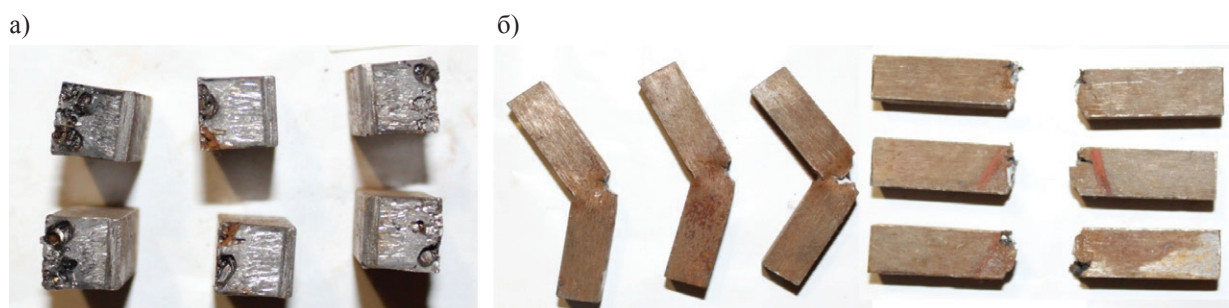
Образцы после испытаний на ударную вязкость: излом образцов для оценки площади дефектов (а); виды изломов образцов (б)
